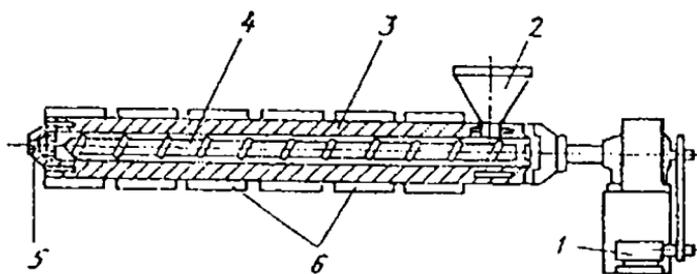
Горизонтальный экструдер: 1 — привод; 2 — бункер; 3 — цилиндр; 4 — червяк; 5 — канал для выхода расплава; 6 — нагреватели
